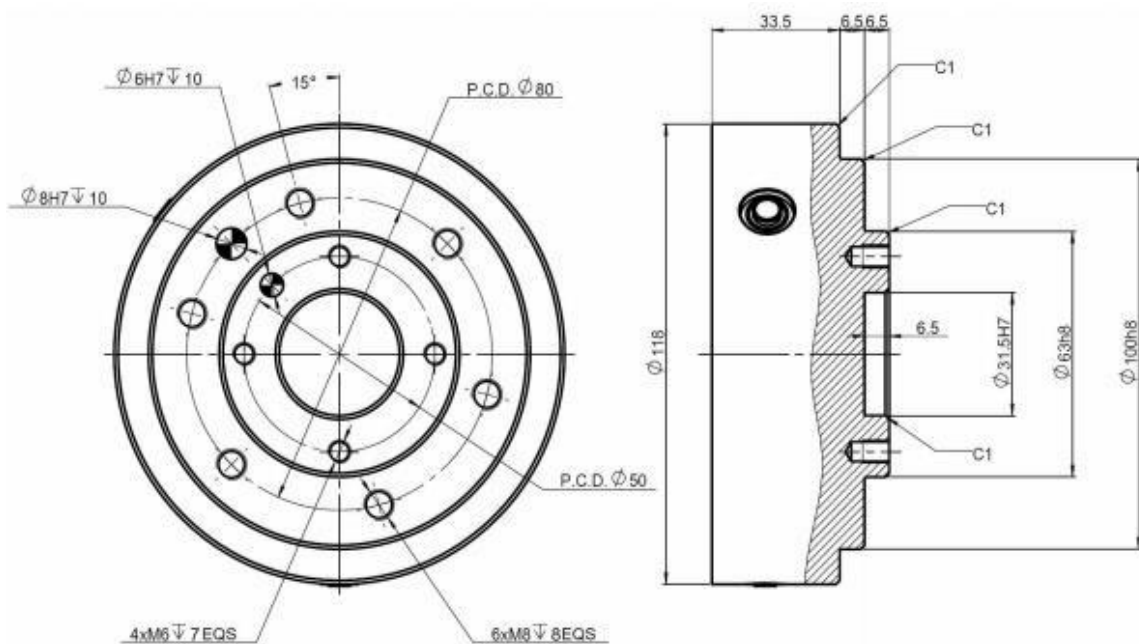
Торцевой фланец для ЯКА Pro 16
